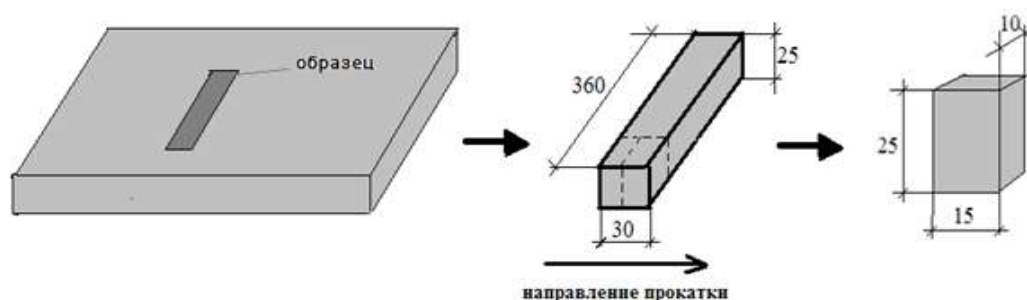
Схема выреза и размеры образца из стали ЕН36 для исследований коррозионной устойчивости
